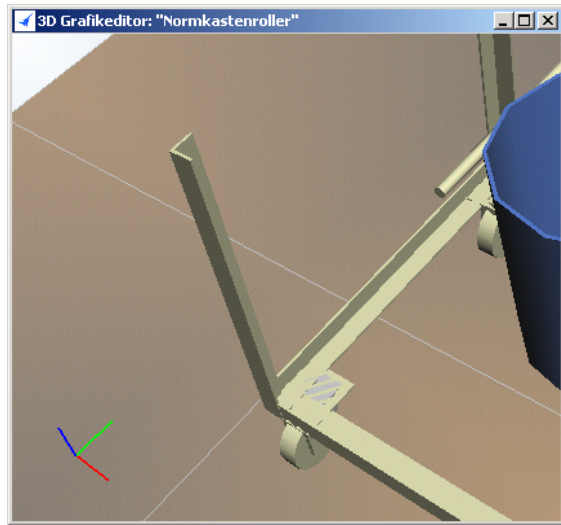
Primitiv mit Einfügewerkzeug genau platzieren
